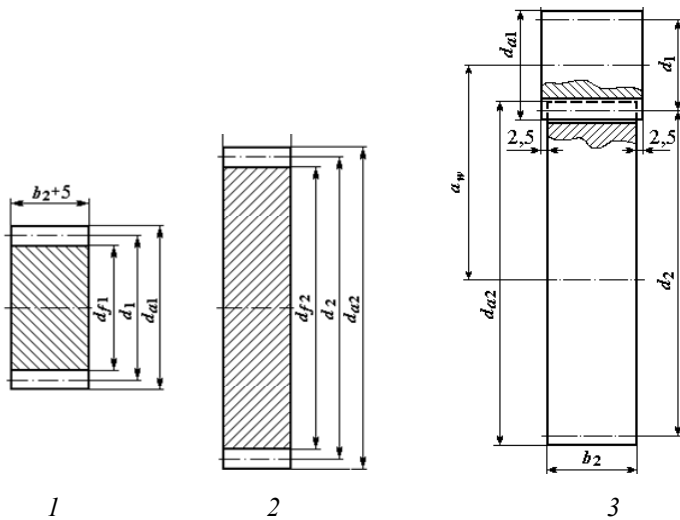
Эскизы шестерни 1, зубчатого колеса 2 и зубчатого зацепления 3
